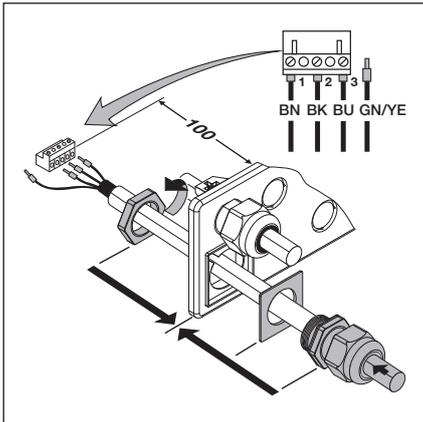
Montage der Motoranschlussleitung in der Verschraubungsflanschplatte
